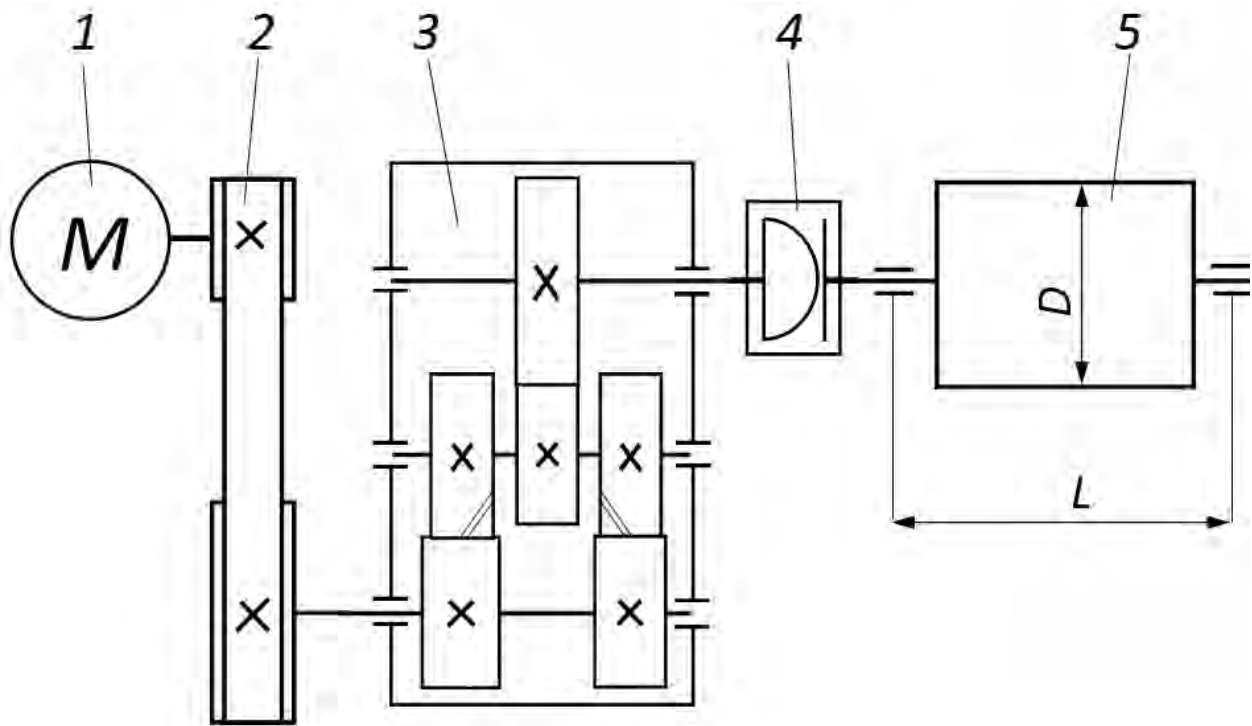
Схема привода ленточного конвейера (вид сверху): 1 – асинхронный электродвигатель; 2 – клиноременная передача; 3 – редуктор цилиндрический двухступенчатый (с косозубой быстроходной ступенью и разделенным потоком мощности и прямозубой тихоходной ступенью); 4 – муфта кулачково-дисковая; 5 – приводной вал с барабаном
